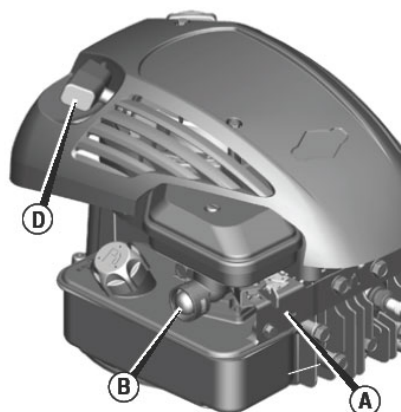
Внешний вид элементов запуска двигателя ЛопЛоша.
